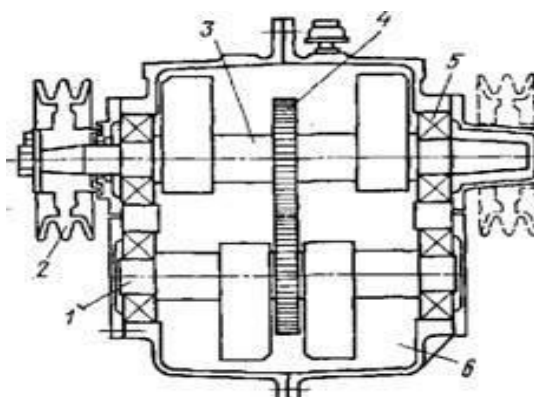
Двухвальний віброблок: 1, 3-ведений та провідний вали з дебалансами; 2 -приводний шків; 4 -шестерні; 5 - підшипники; 6 - масляна ванна.
